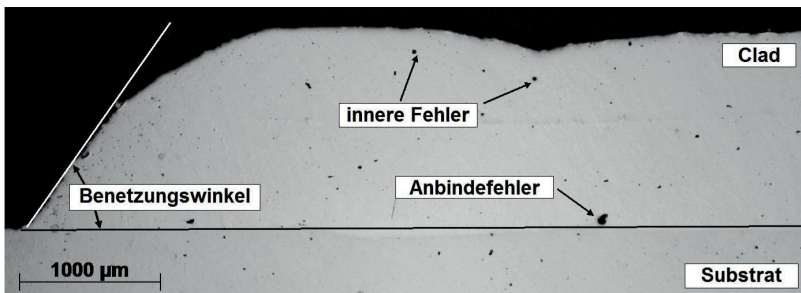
Schichtfehler und Benetzungswinkel einer Auftragschweißung
